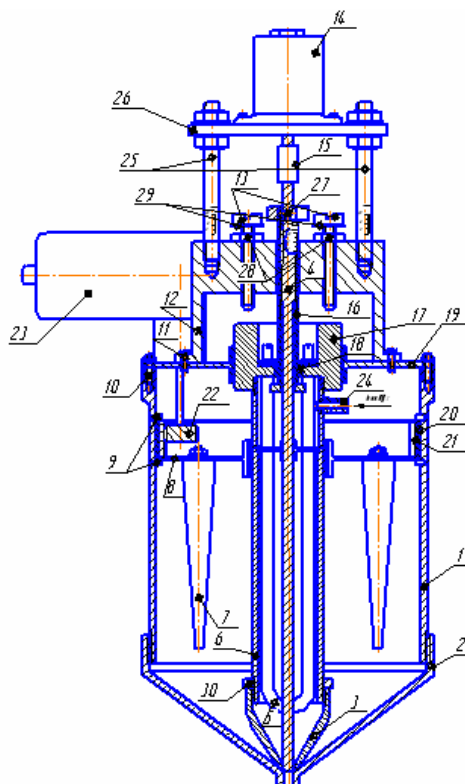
Схема устройства бункера-дозатора для подачи порошковых композиций:
